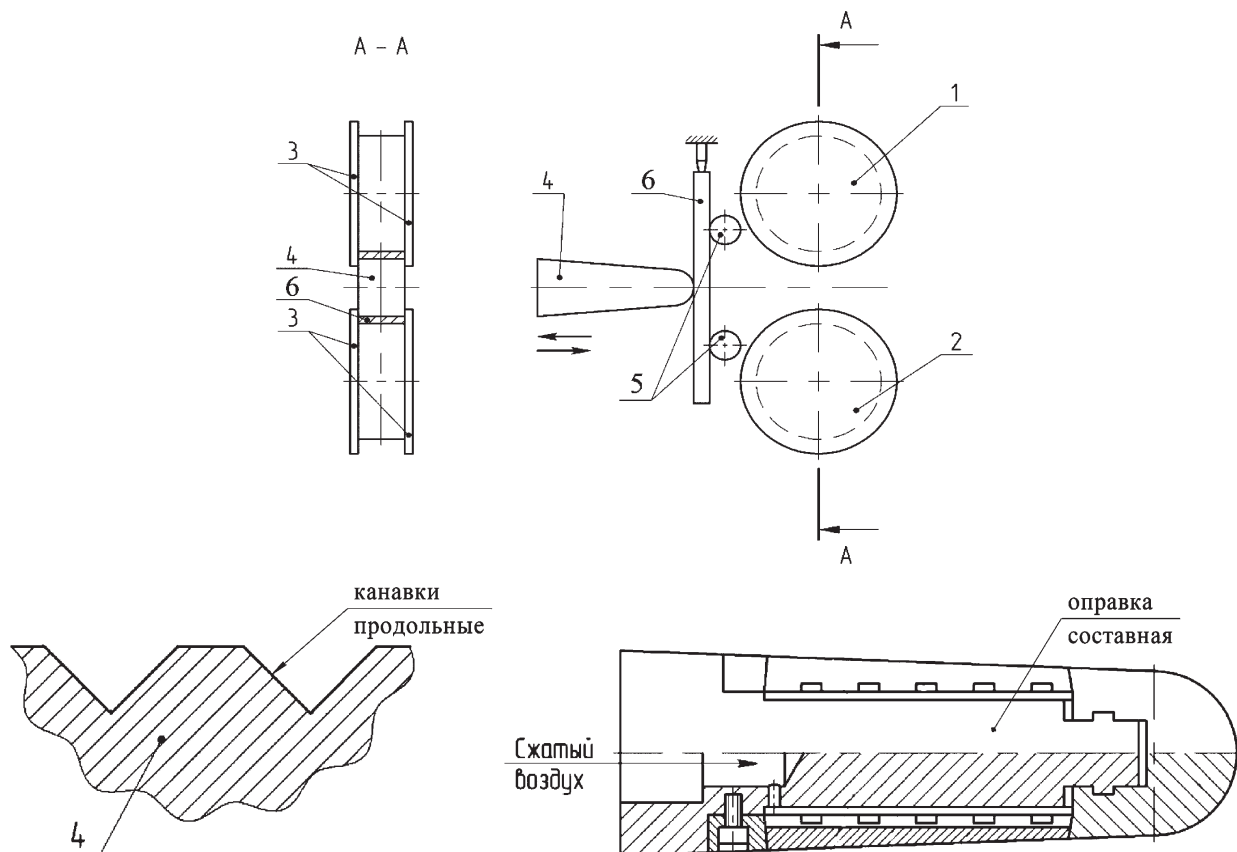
Схема прокатки профиля на оправке: 1, 2 – валки; 3 – реборды; 4 – оправка; 5 – ролики; 6 – прокатываемая полоса
